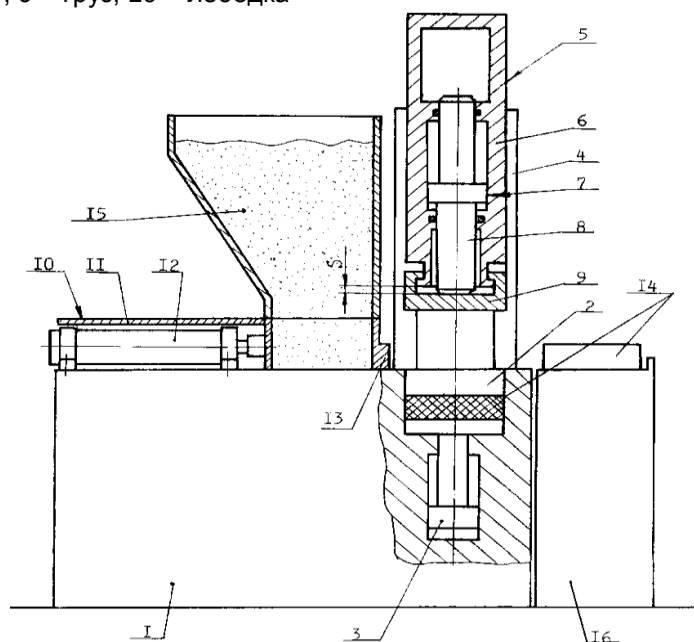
Установка ударного прессования кирпичей [7], автор Брагин В. Н.: 1 – станина; 2 – камера прессования; 3 – выталкиватель; 4 – кронштейн; 5 – механизм прессования; 6 – ползун; 7 – ударный механизм; 8 – ударник; 9 – пуансон; 10 – механизм подачи сыпучего материала; 11 – дозатор; 12 – гидроцилиндр; 13 – выступом; 14 – готовое изделие; 15 – бункер; 16 – транспортер
